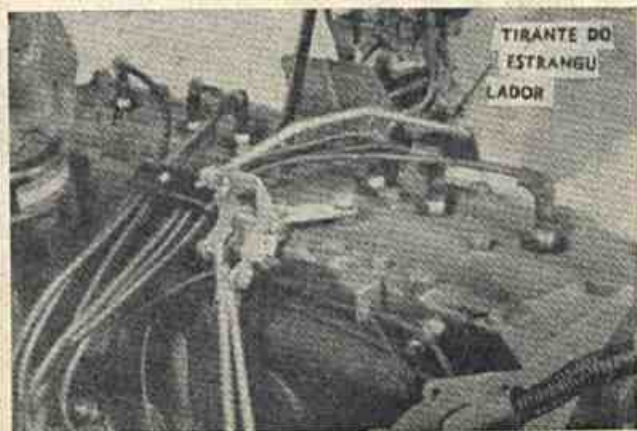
Posição da haste do estrangulador do carburador no motor de 6 cilindros.
